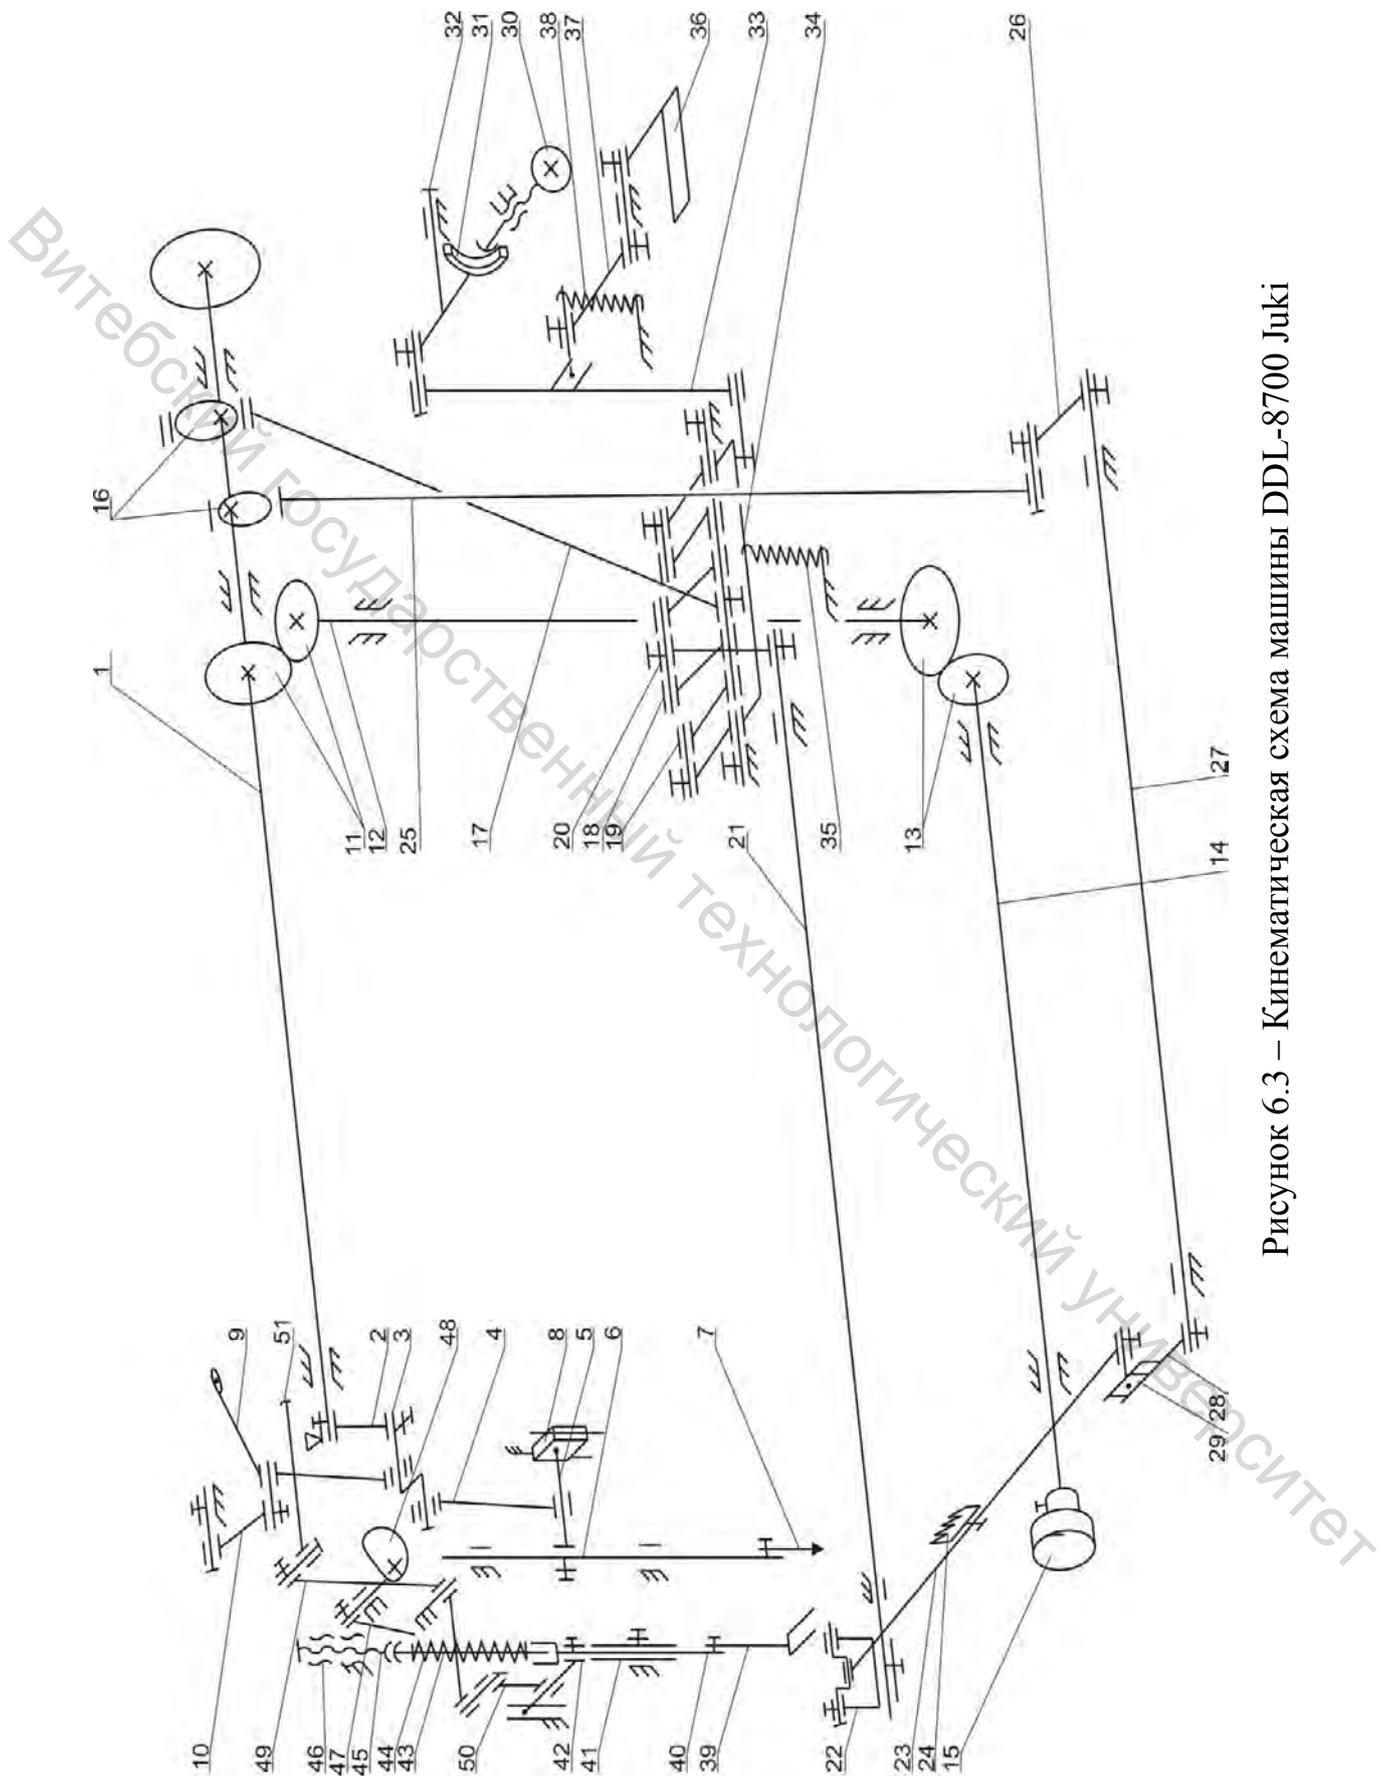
Кинематическая схема машины DDL-8700 Juki
